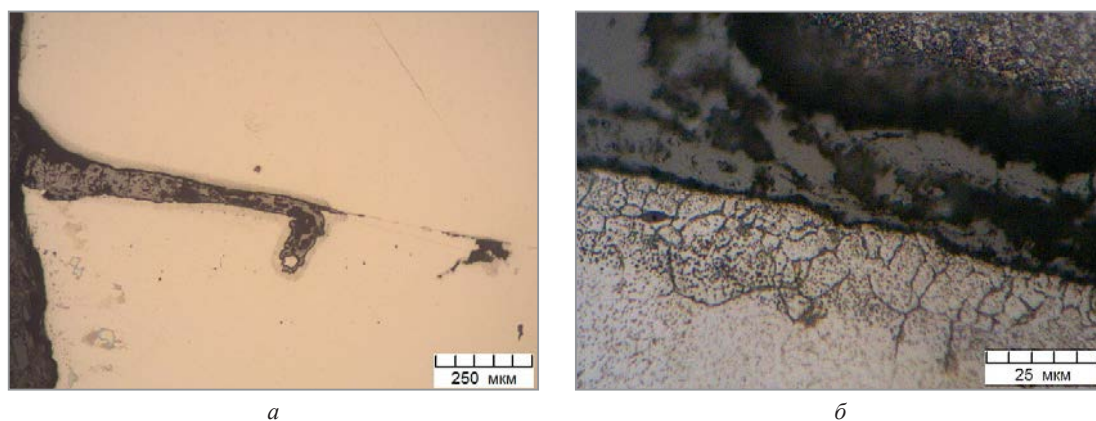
Дефекты сварного шва; образец 1; *а* – несплошность; *б* – пережог.
